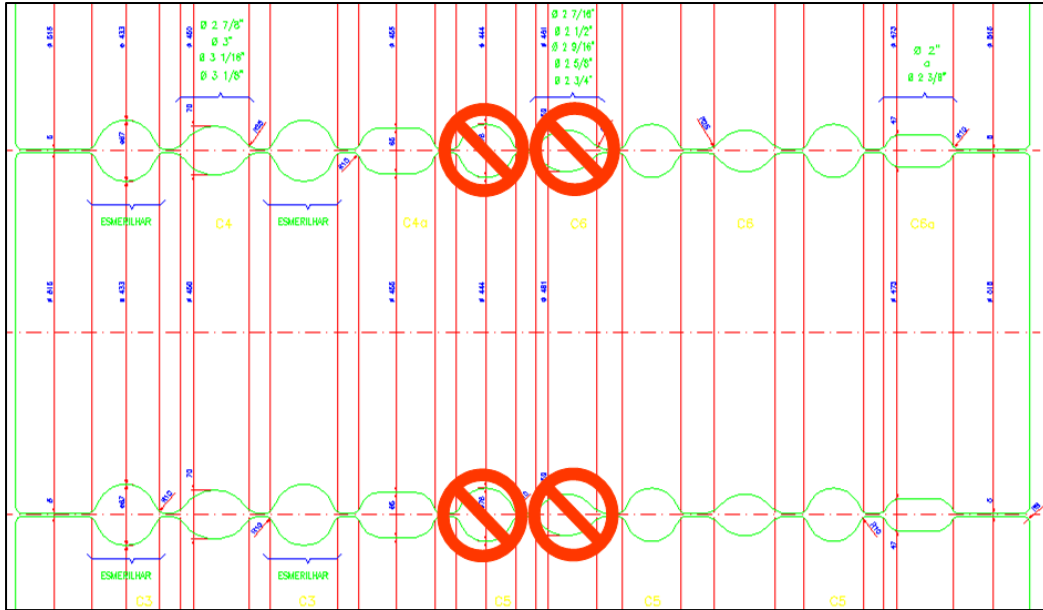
Proposta de alteração do plano de passes da cadeia 2.
